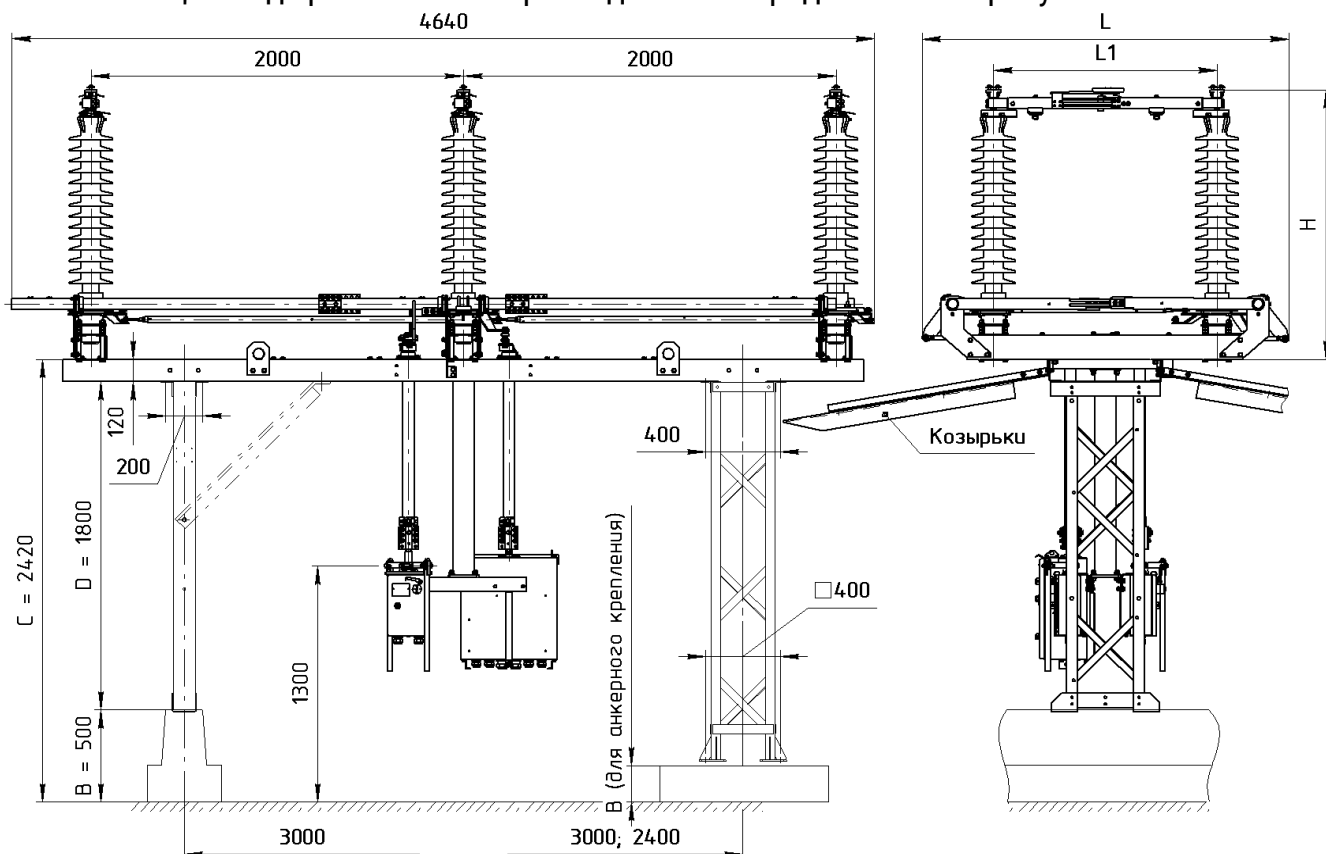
Общий вид трехполюсного разъединителя РН СЭЩ®-110
